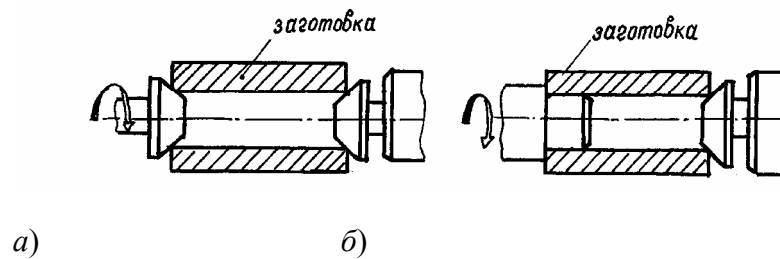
Закрепление заготовки при помощи поводкового центра – "ерша" (а), схема обозначения (б):
